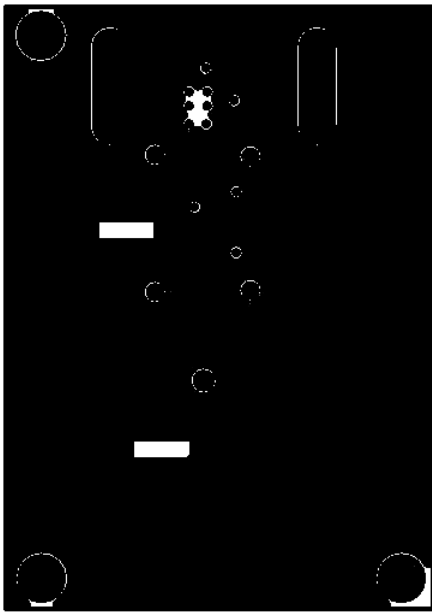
MAX3744/MAX3745 评估板 PCB 布线
